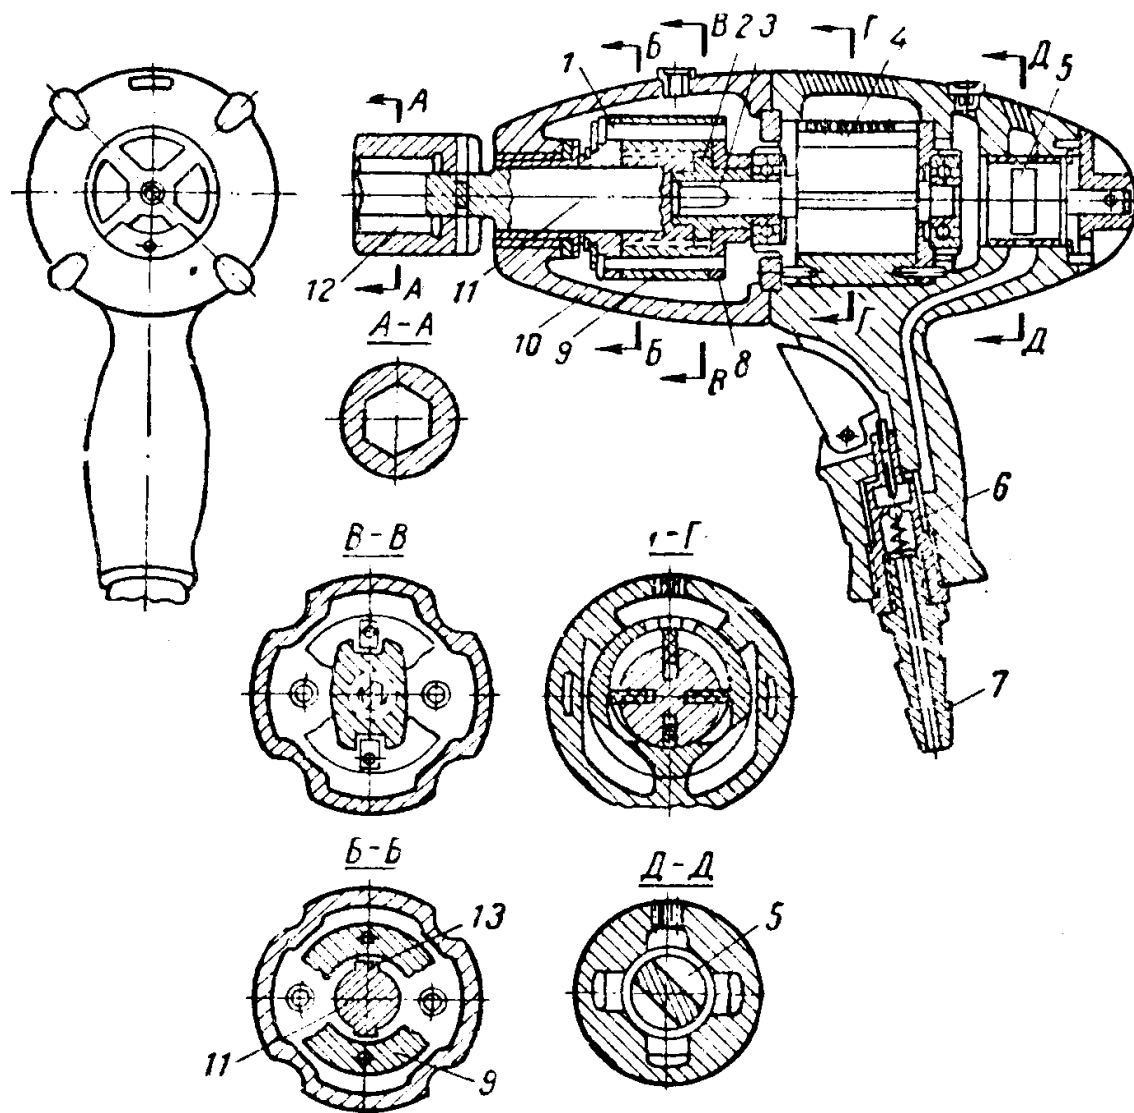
Пневматичний інерційно-ударний гайковерт
